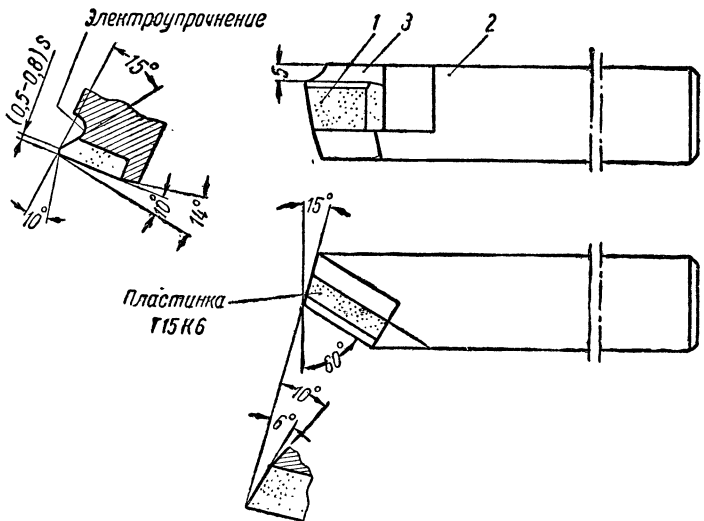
Подрезной резец конструкции токаря-новатора В. А. Колесова.
